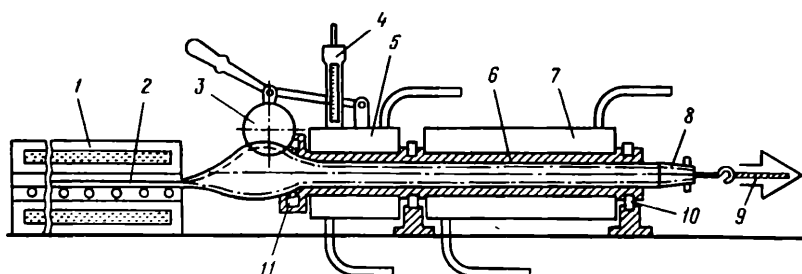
Схема изготовления пластмассовых труб из листовой заготовки:
